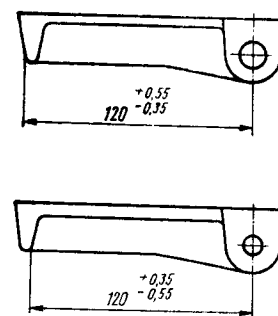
Пример назначения допусков на размер между осевой линией и необрабатываемой поверхностью, когда штамповка производится в одной половине штампа.
